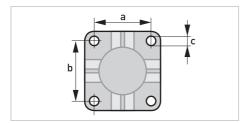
Dimensions pour plaque de montage du boîtier intempéries
